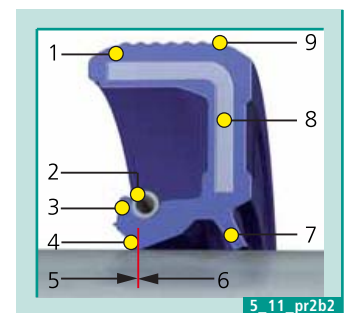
Querschnitt eines Radialwellendichtrings mit zwei Dichtlippen; 1 Haftteil, 2 Zugfeder, 3 Dichtlippe, 4 Dichtkante, 5 Stirnseite, 6 Bodenseite, 7 Schutzlippe, 8 Versteifungsring, 9 Aussenmantel.
